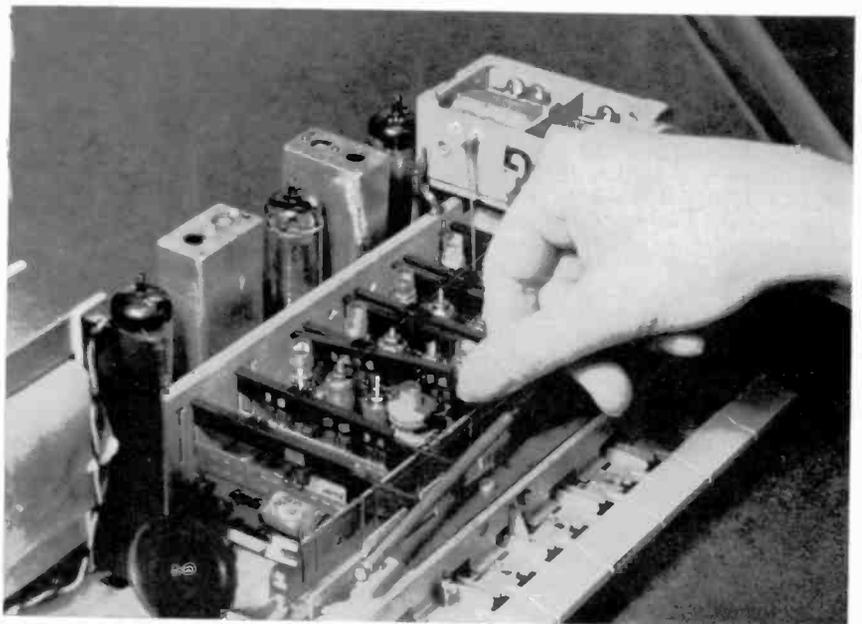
So leicht lassen sich die Drucktastenschieber des 1098 auswechseln
